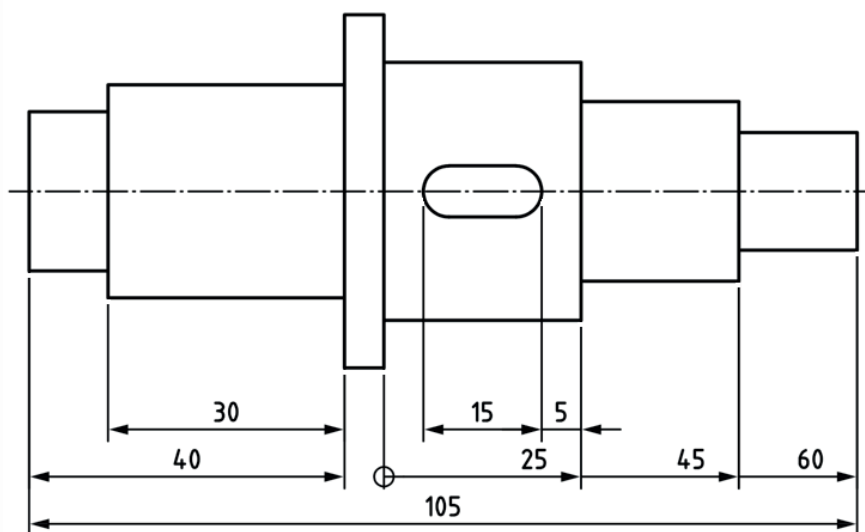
Cotagem combinada (paralela, aditiva e simples dimensões)
